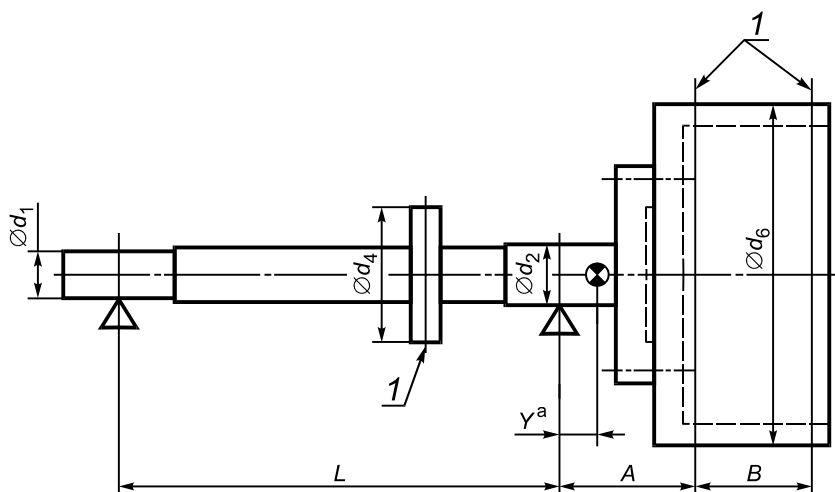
Контрольный ротор типа В для испытаний на горизонтальном балансировочном станке
